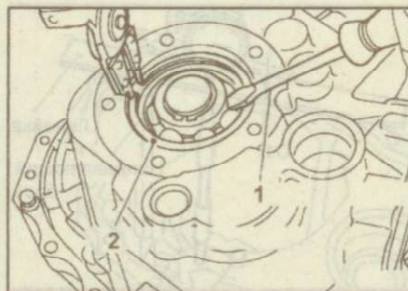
Использование пассатижей и отвертки (1) для установки стопорного кольца (2) крепления подшипника
